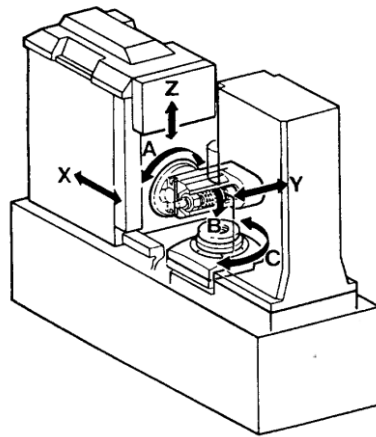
Схема зубофрезерного верстата з шістьма керованими осями.
